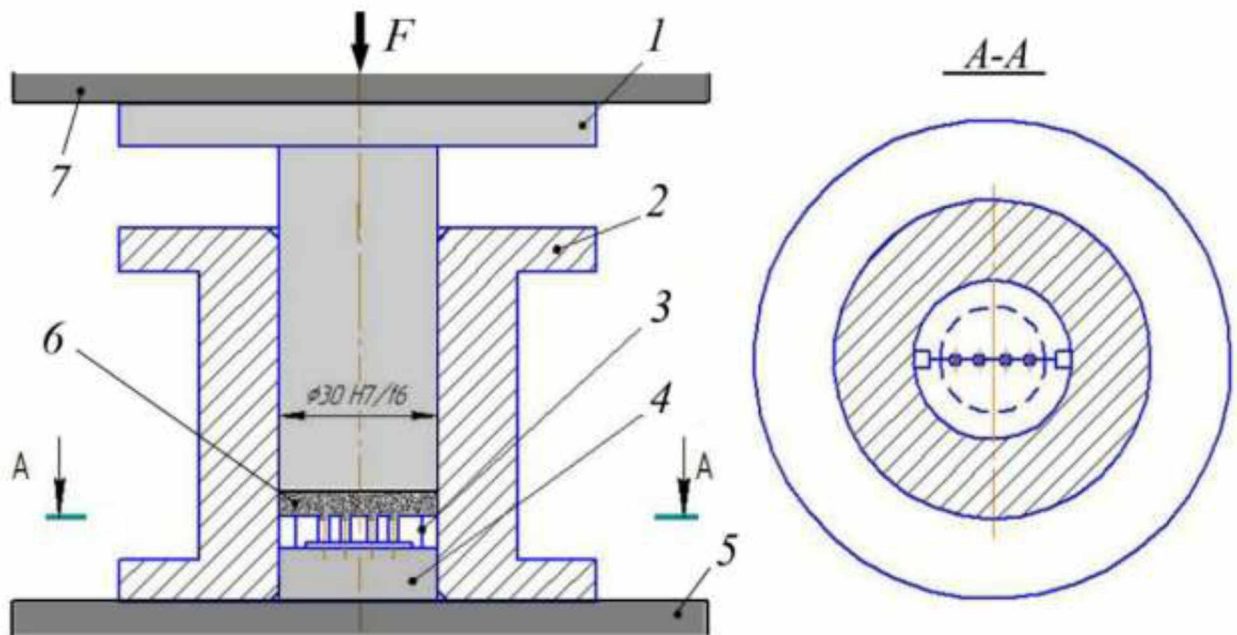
Прес-форма для формування зразків для триботехнічних випробувань: 1, 4 - пуансони; 2 - матриця; 3 - рознімний формоутворювальний блок; 5, 7 - нижня і верхня плити преса; 6 - навіска грануляту полімеру
